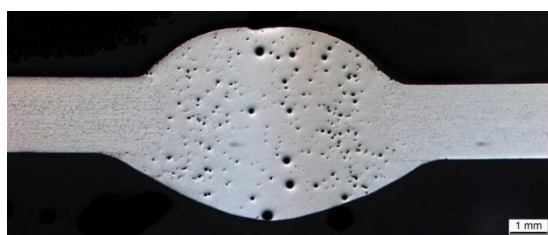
Микрошлиф сварного шва, выполненного проволокой диаметром 1,6 мм
